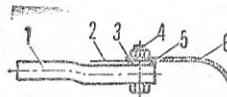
Узел латы: 1 — лата, 2 — полотнище паруса, 3 — лонжерон, 4 — болт крепления, 5 — люверс шкаторины, 6 — лобовой полуконус.
